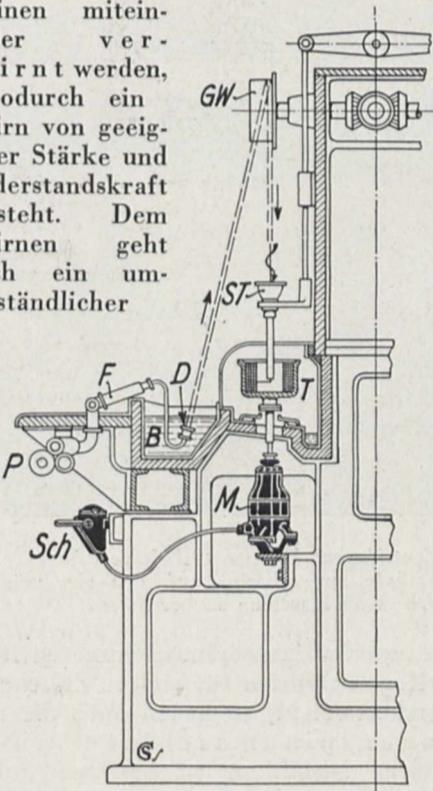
Topfspinmaschine für Viskoseseide im Querschnitt
